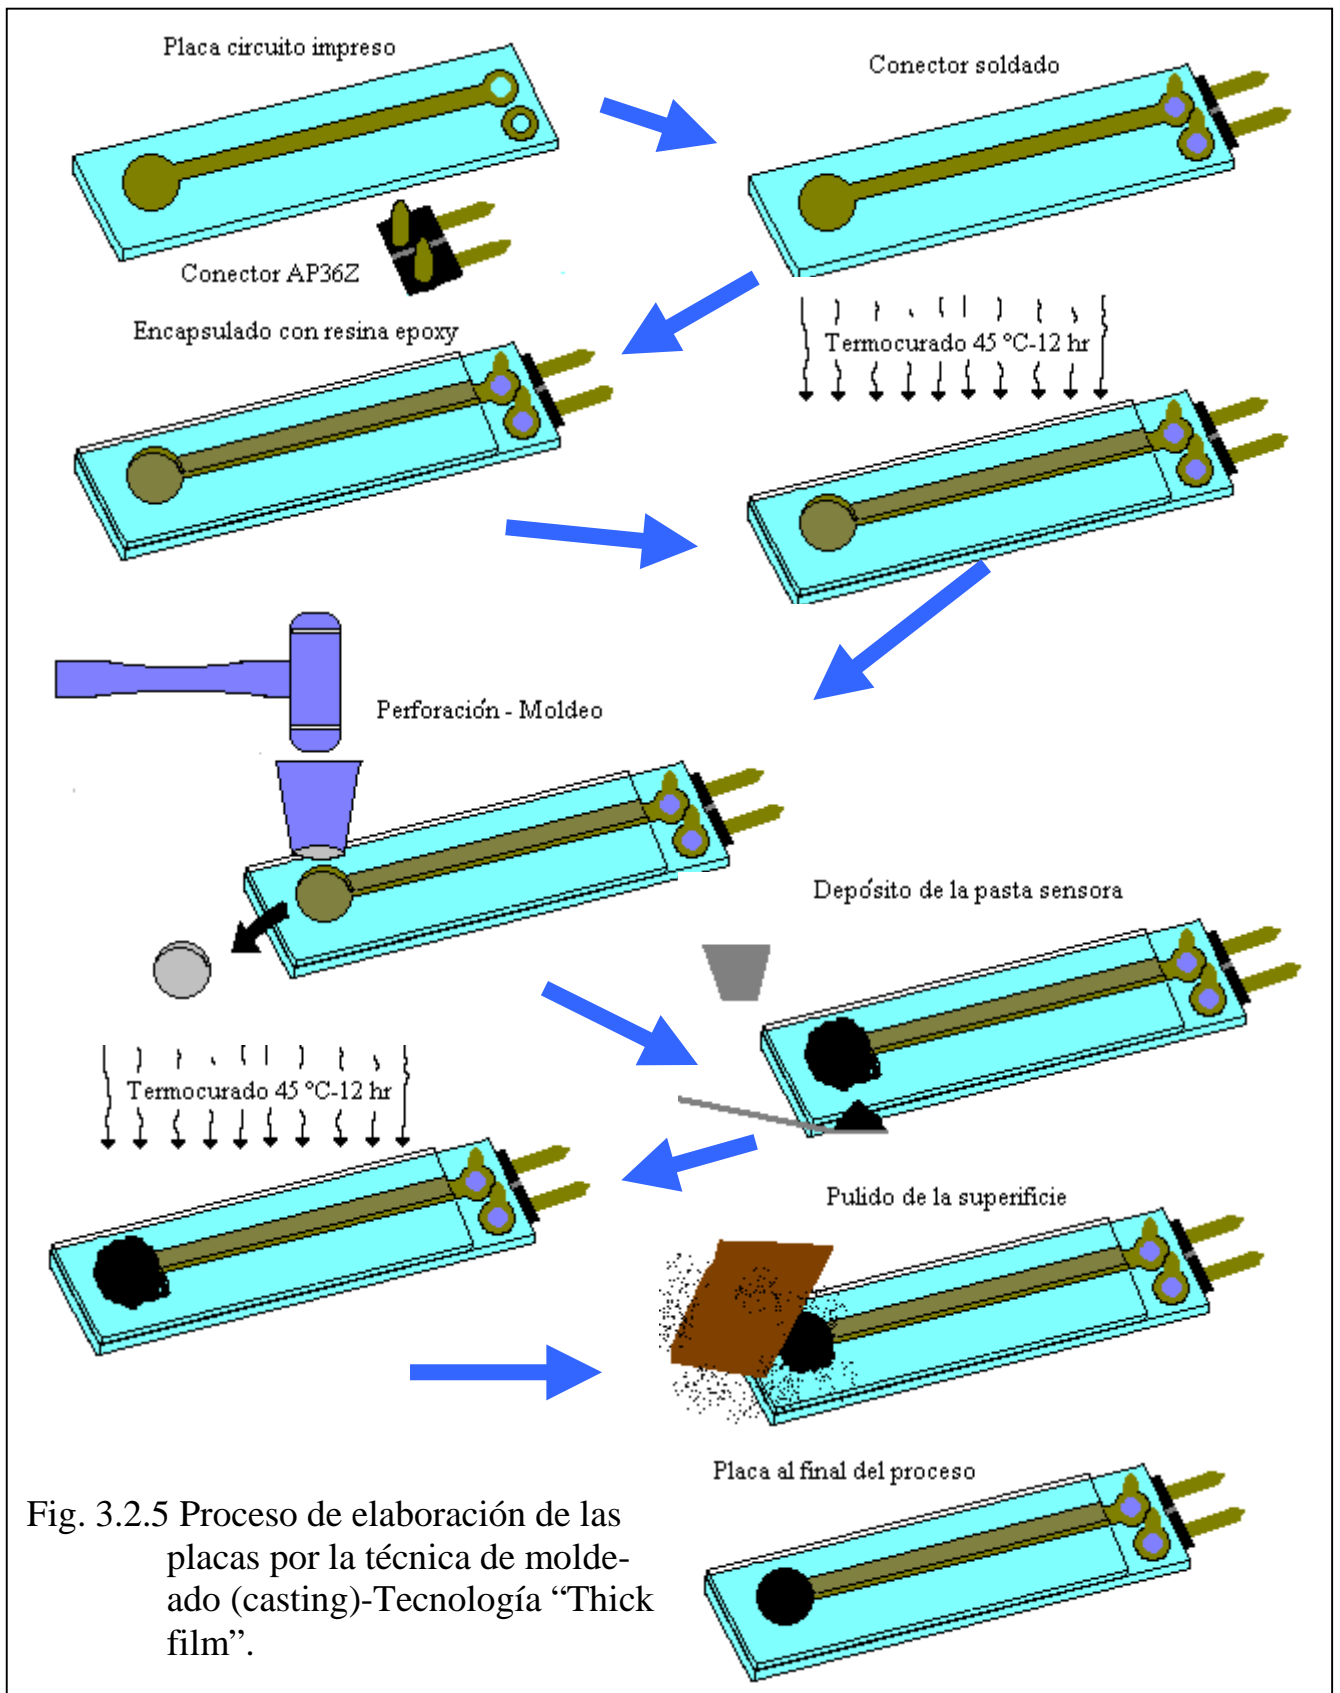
Proceso de elaboración de las placas por la técnica de moldeado (casting)-Tecnología "Thick film".
